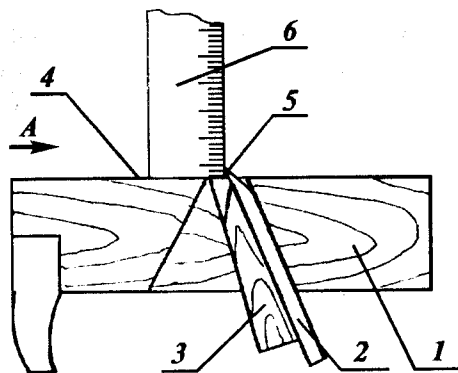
Измерение высоты расположения режущей кромки: 1 — колодка; 2 — нож; 3 — клин; 4 — подошва; 5 — режущая кромка; 6 — линейка
